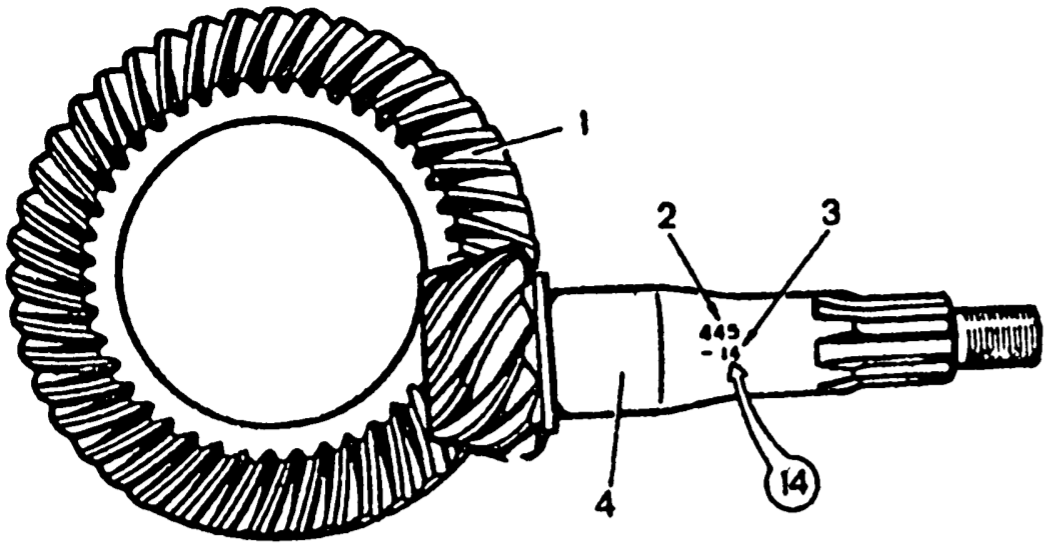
Шестерни главной передачи: 1 - ведомая шестерня; 2 - порядковый номер; 3 - поправка в сотых долях миллиметра номинальному положению; 4 - ведущая шестерня
